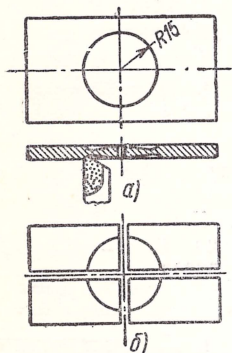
Схема обработки отрезных резцов тангенциального типа
